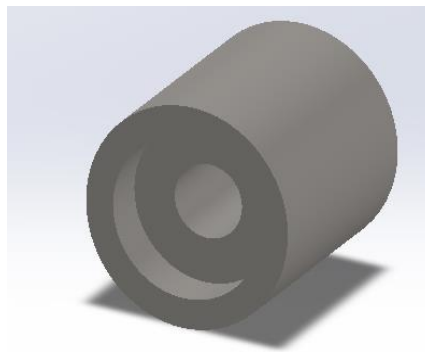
Vista de pieza N°8 (Fuente 96)
